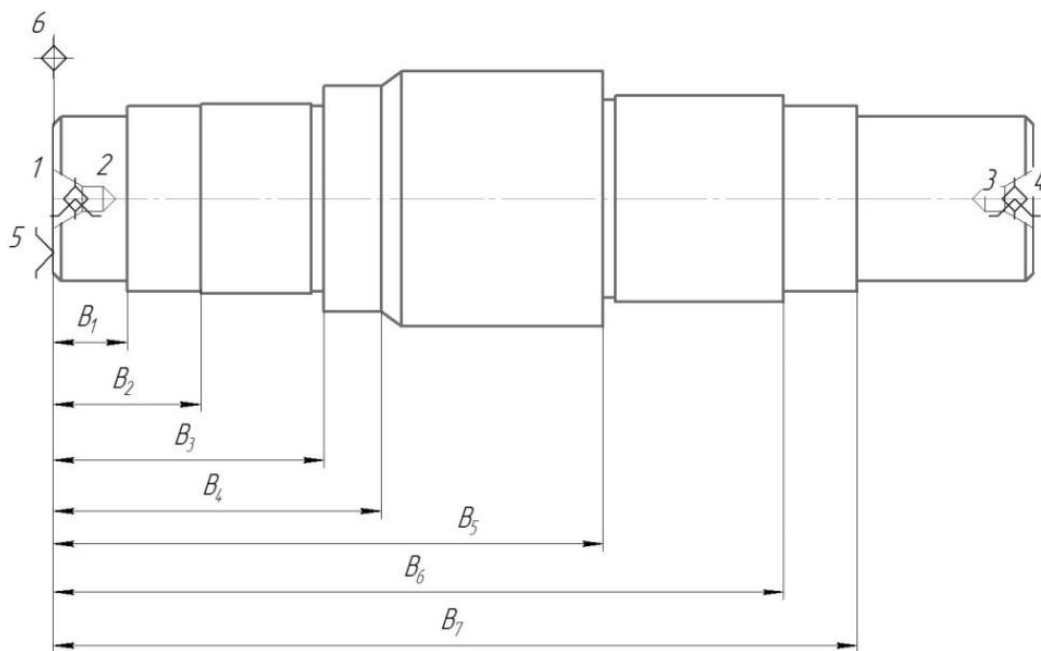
Ескіз механічної обробки зі схемою базування (чистові бази)
